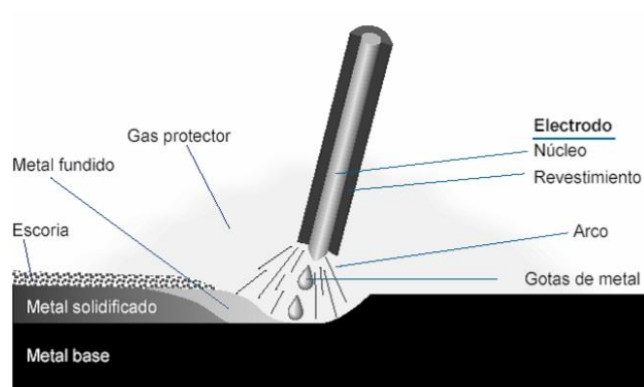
Detalle del proceso de soldadura SMAW
